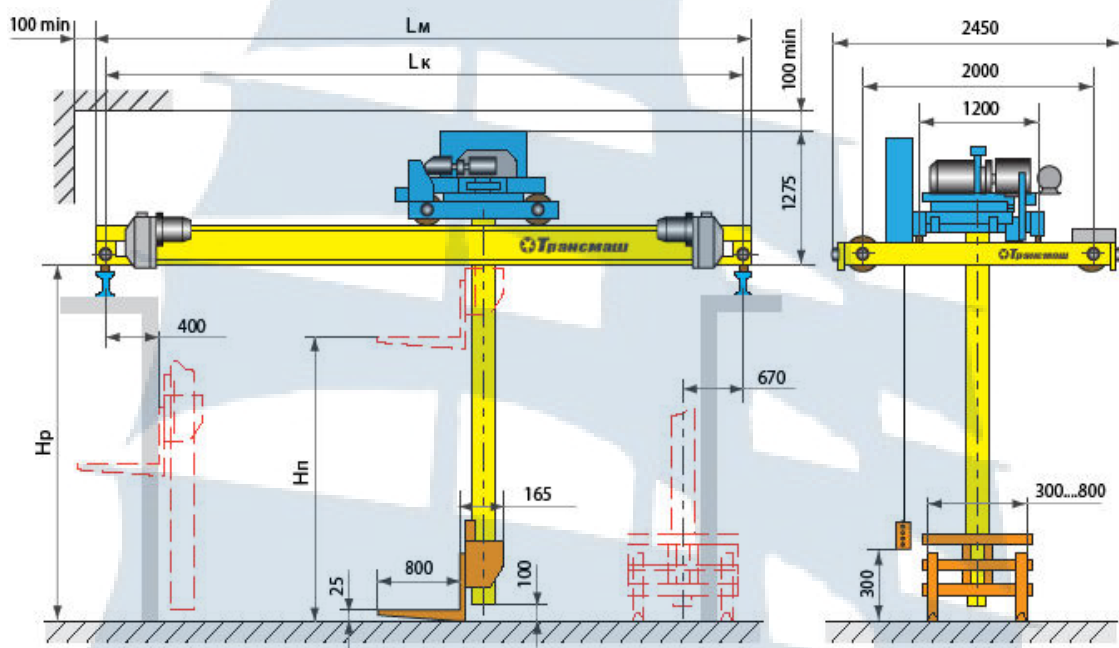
Схема крана-штабелёра мостового электрического грузоподъёмностью 1 тонна
